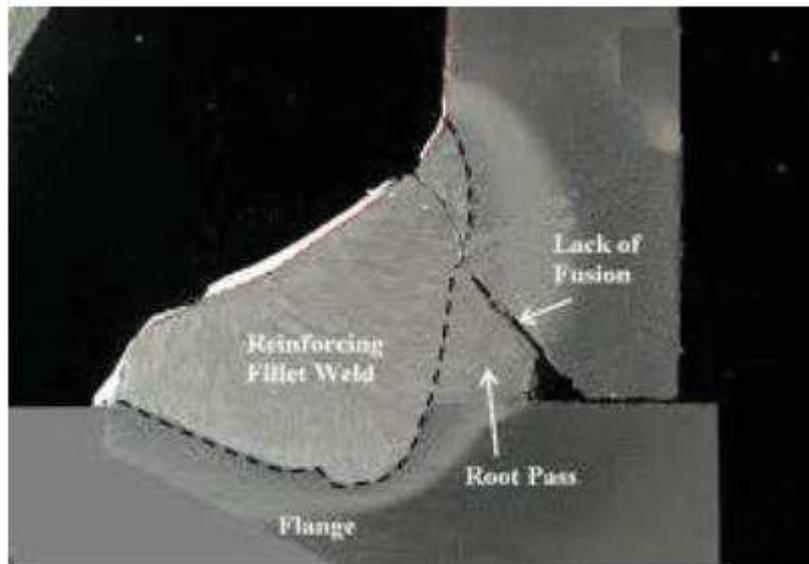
Manque de fusion à la racine de la soudure.
